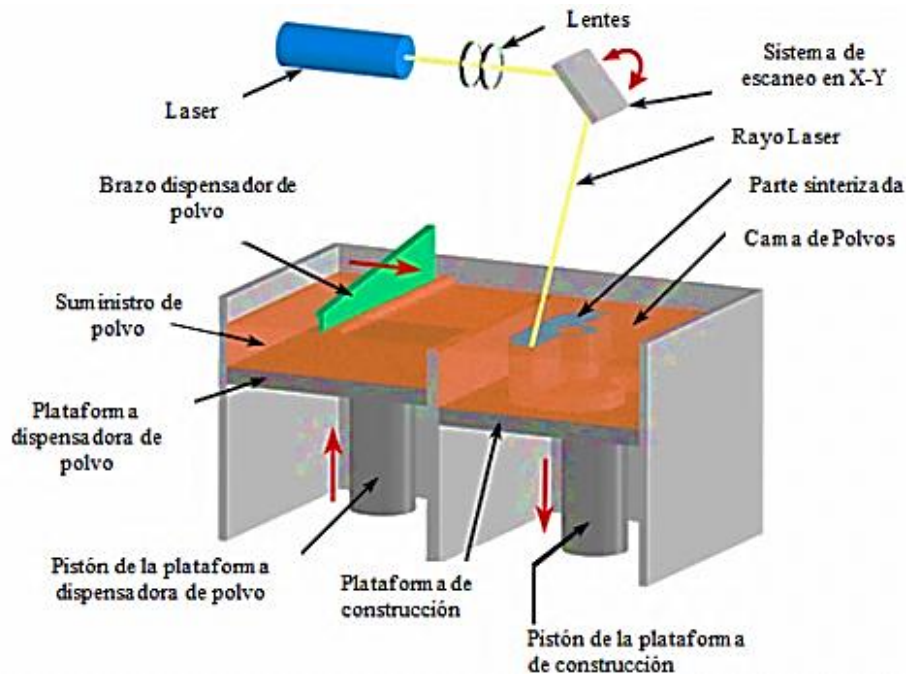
Los diferentes componentes de una impresora de Sinterizado Selectivo por Laser (SLS) Fuente: <http://www.3dnatives.com/es/sinterizado-directo-de-metal-por-laser-les-explicamos-todo/>
